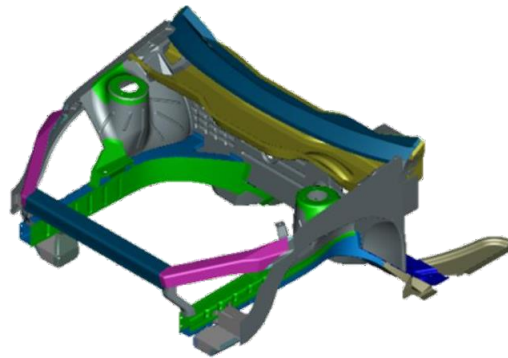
Зібрана передня частина нижньої конструкції з використанням точкового зварювання.
